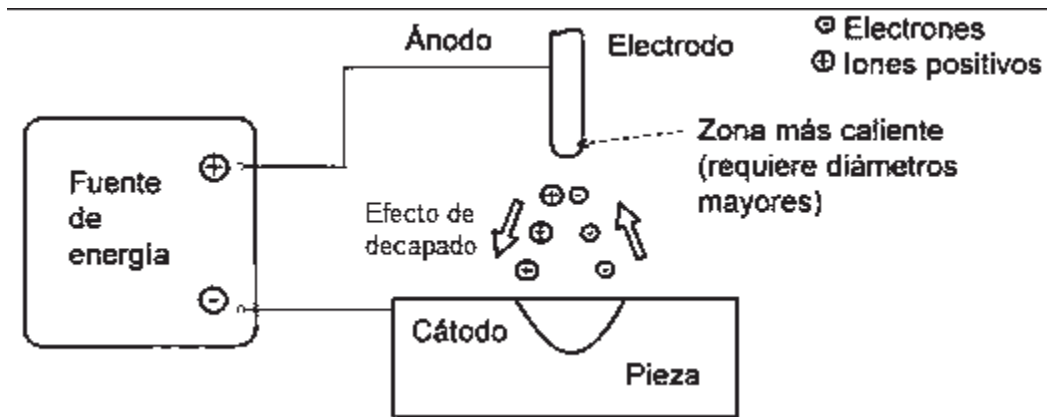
Uso de la polaridad inversa en soldadura del aluminio
